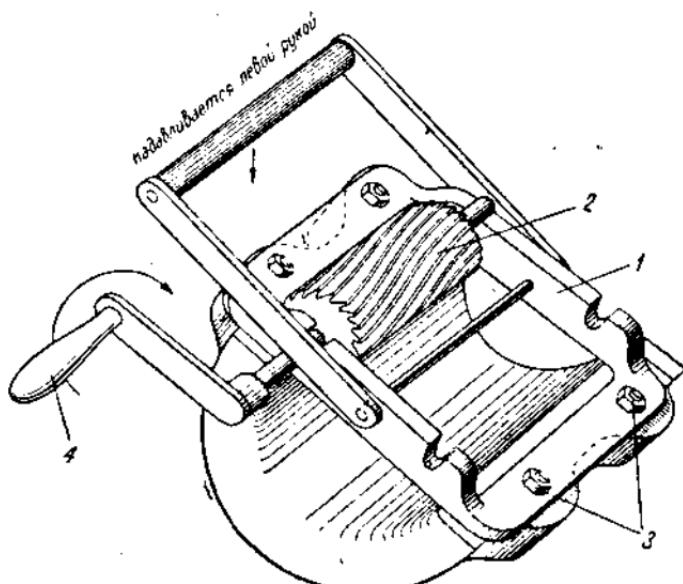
Приспособление для фрезерования холодильников в подшипнике.
